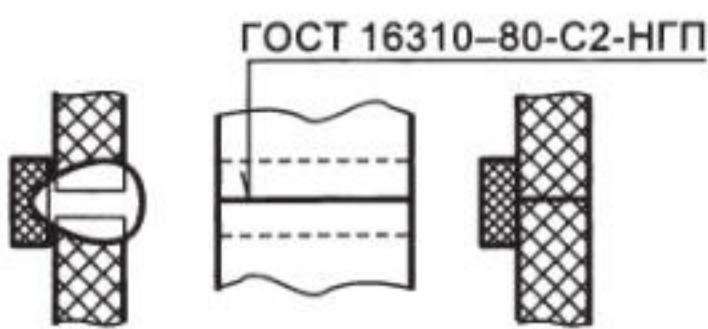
Шов стыкового соединения без скоса кромок, односторонний, на подкладке, выполняемый сваркой нагретым газом с присадкой
